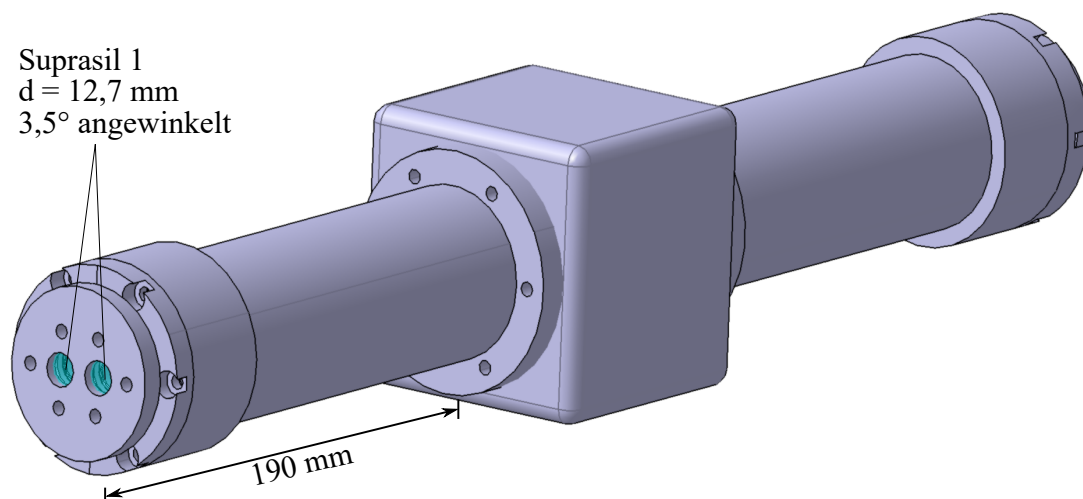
3D-Modell des für TIPS mit Xe neu entwickelten Kaltgaszellendesigns.
